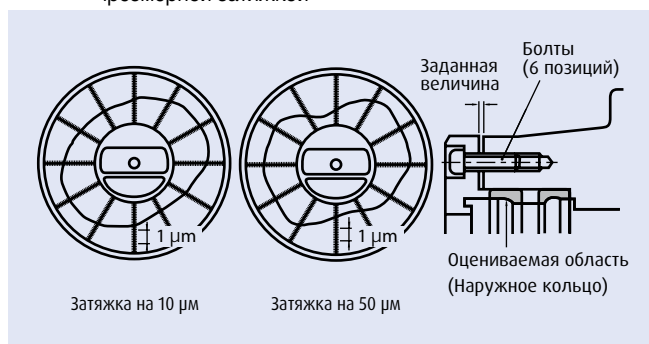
Деформация наружного кольца двухрядного цилиндрического роликового подшипника, вызванная чрезмерной затяжкой
